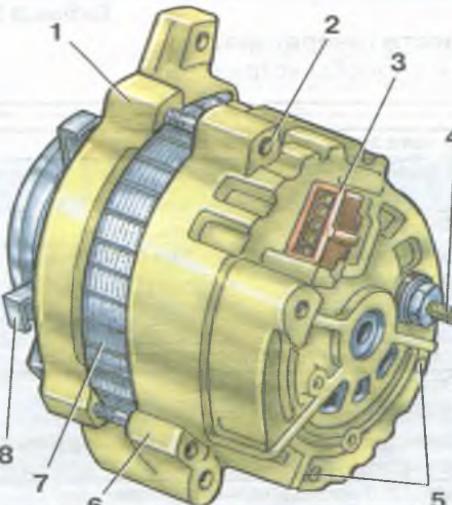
Общий вид генератора: 1 – передняя крышка; 2 – стяжные болты; 3 – колодка выводов «S», «F», «L», «P» генератора; 4 – вывод «B+»; 5 – заклепки; 6 – задняя крышка; 7 – пакет железа статора; 8 – крыльчатка вентилятора
